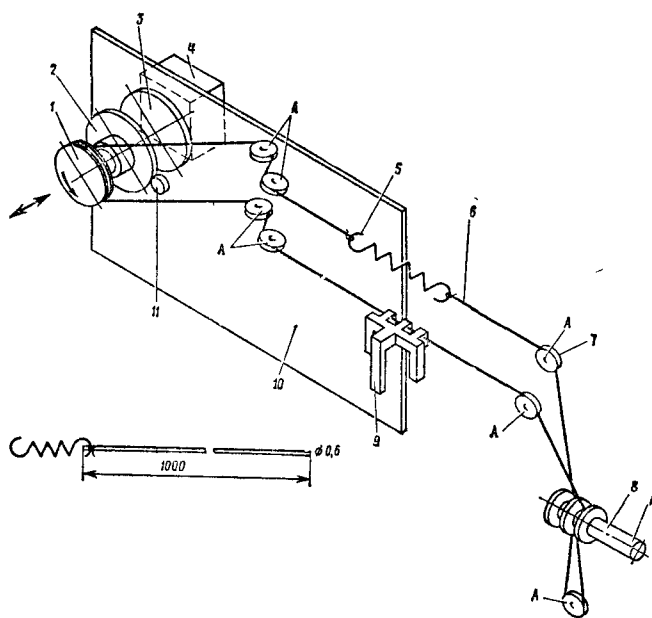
Кинематическая схема верньерного устройства магнитолы «Beta-331»:
